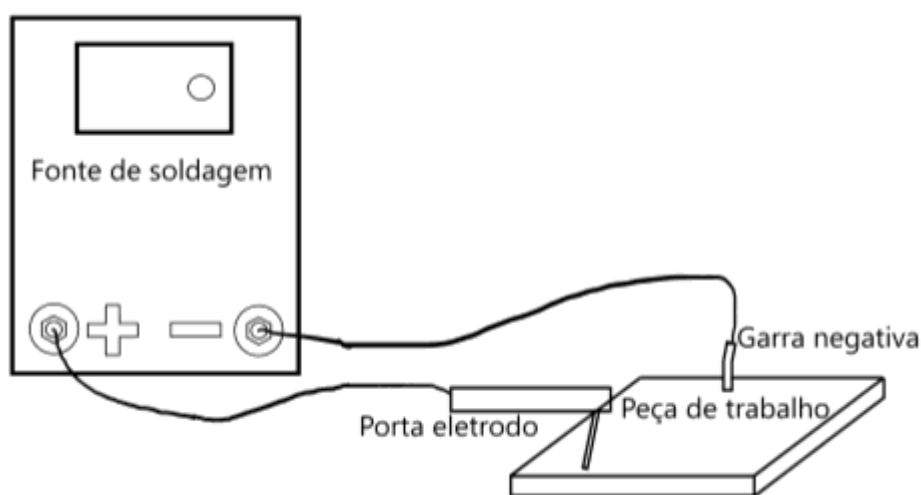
Conexão para soldagem com Eletrodo Revestido.
